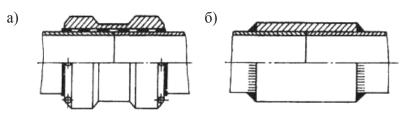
Схемы неразъемных соединений трубопроводов, выполненных с помощью пайки (а) и сварки (б)
